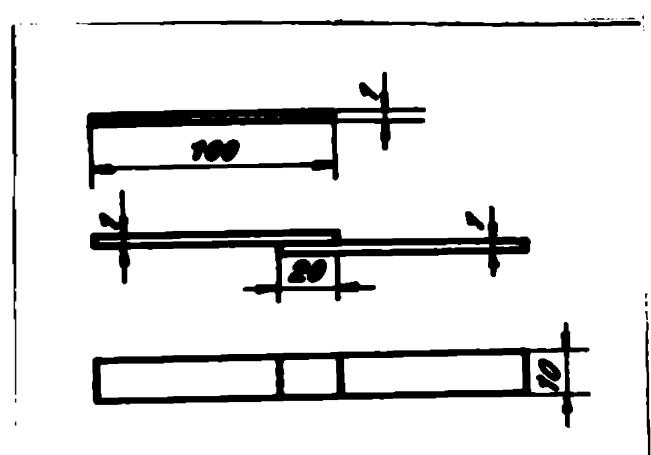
Dimensiunile epruvetelor din tablă de aluminiu pentru cercetări experimentale
